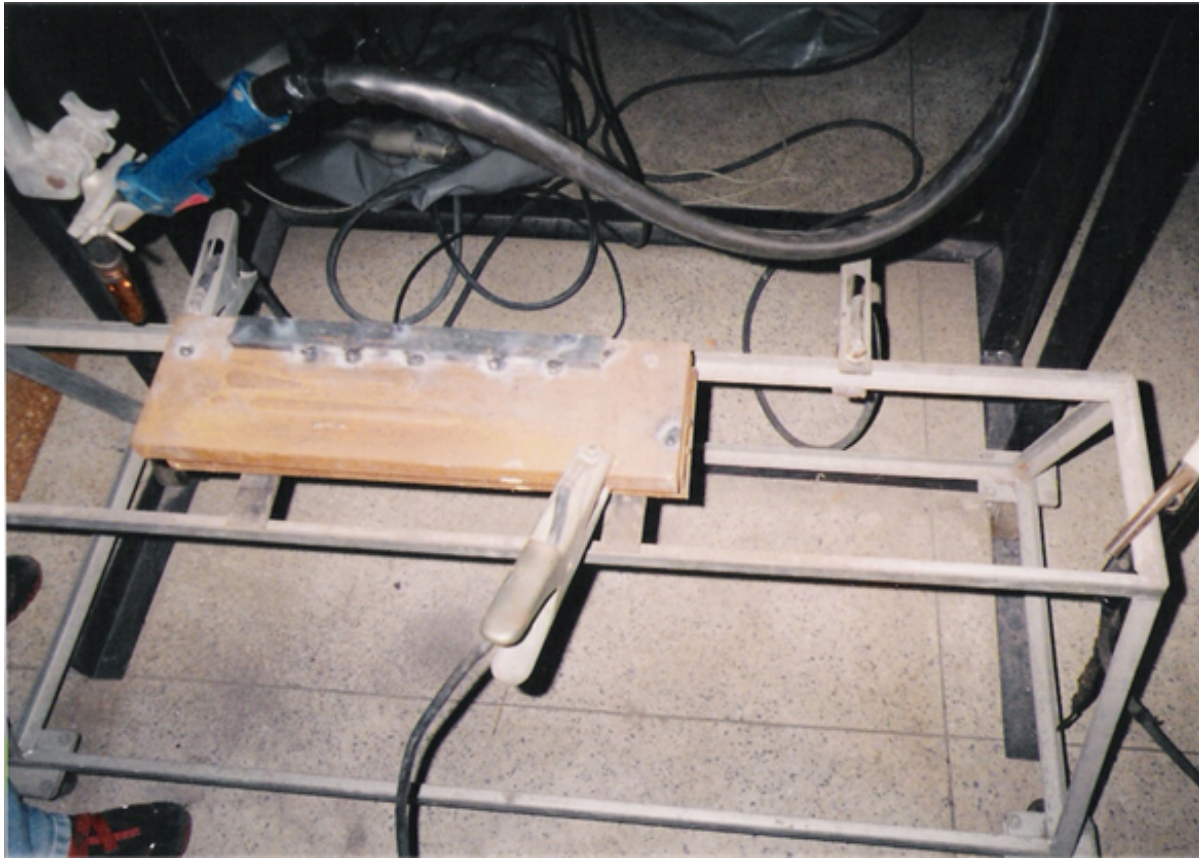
Pistola de soldagem em posição inicial para início da operação.
